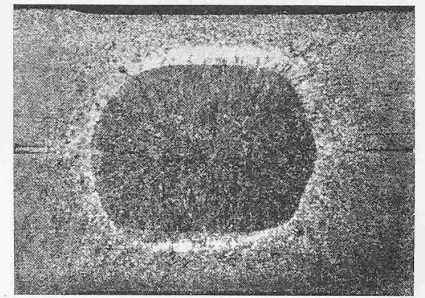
Schliff durch einen Schweisspunkt von zwei Stahlblechen zu je 10 mm Stärke
